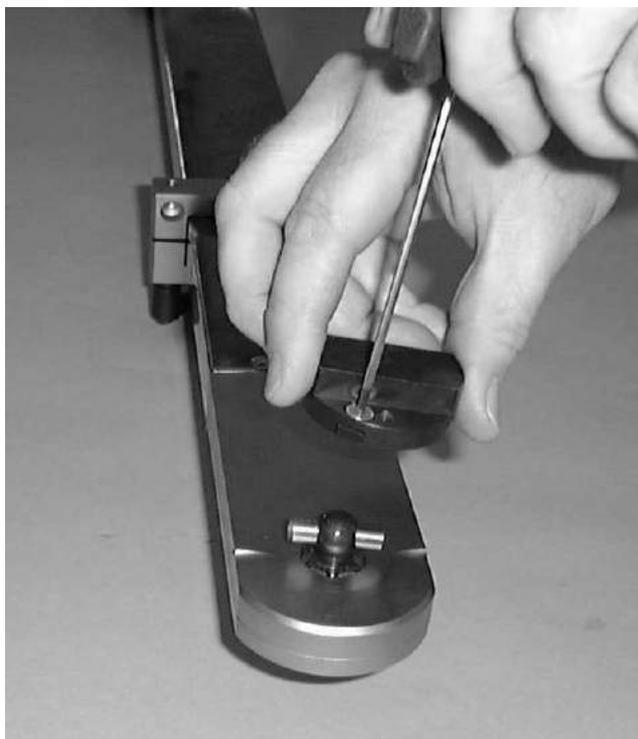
Установка шарового соединения на шпиндель станка
